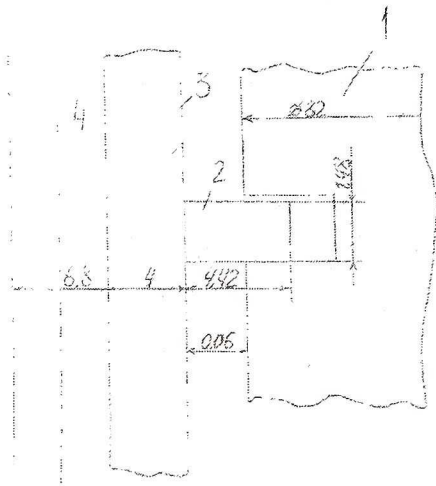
Схема контакта верхнего поршневого кольца двигателя ВАЗ-21083 со стенкой цилиндра; 1 - поршень, 2 - поршневое кольцо, 3 - гильза цилиндра, 4 - канал охлаждающей жидкости.
